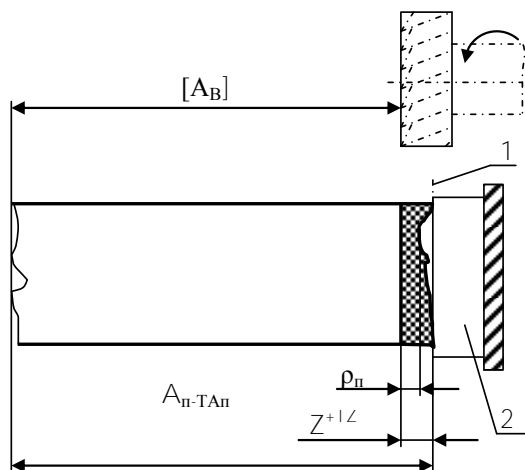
Схема удаления припуска на операции фрезерования с поверхности, являющейся базой
